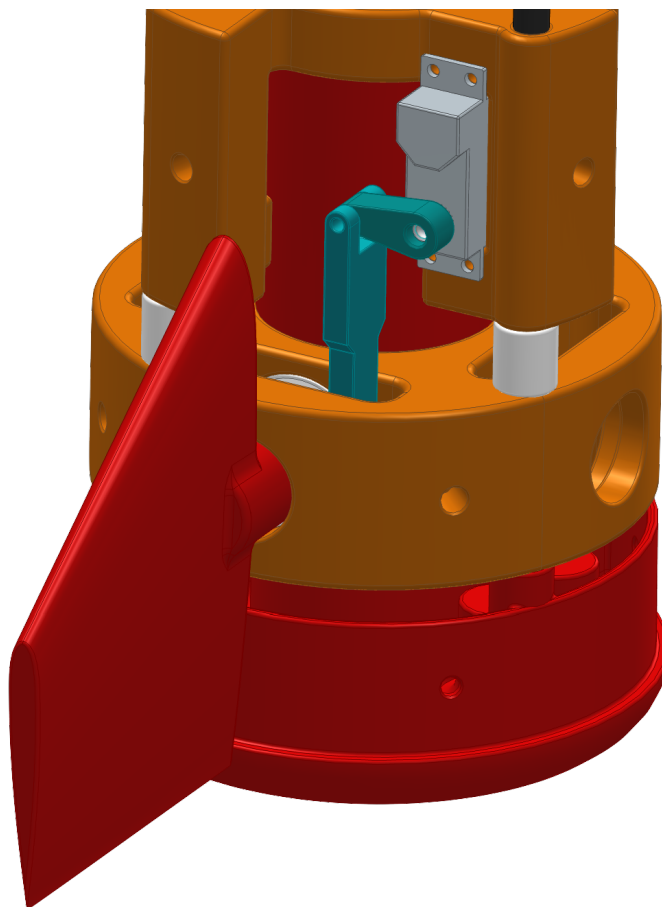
Assembly des kompletten Finnensteuermechanismus
